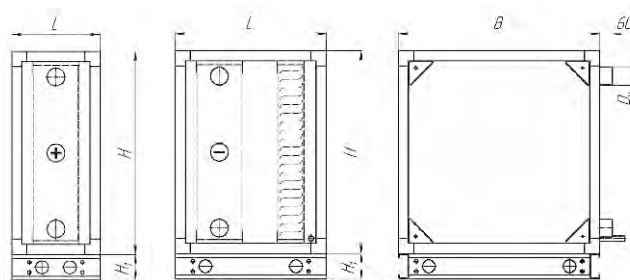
Габаритные размеры. Блок воздухоохладителя непосредственного испарения.
